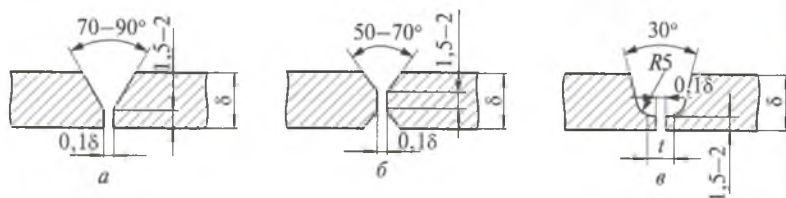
Виды разделки кромок при сварке стыковых швов разных толщин металла:
